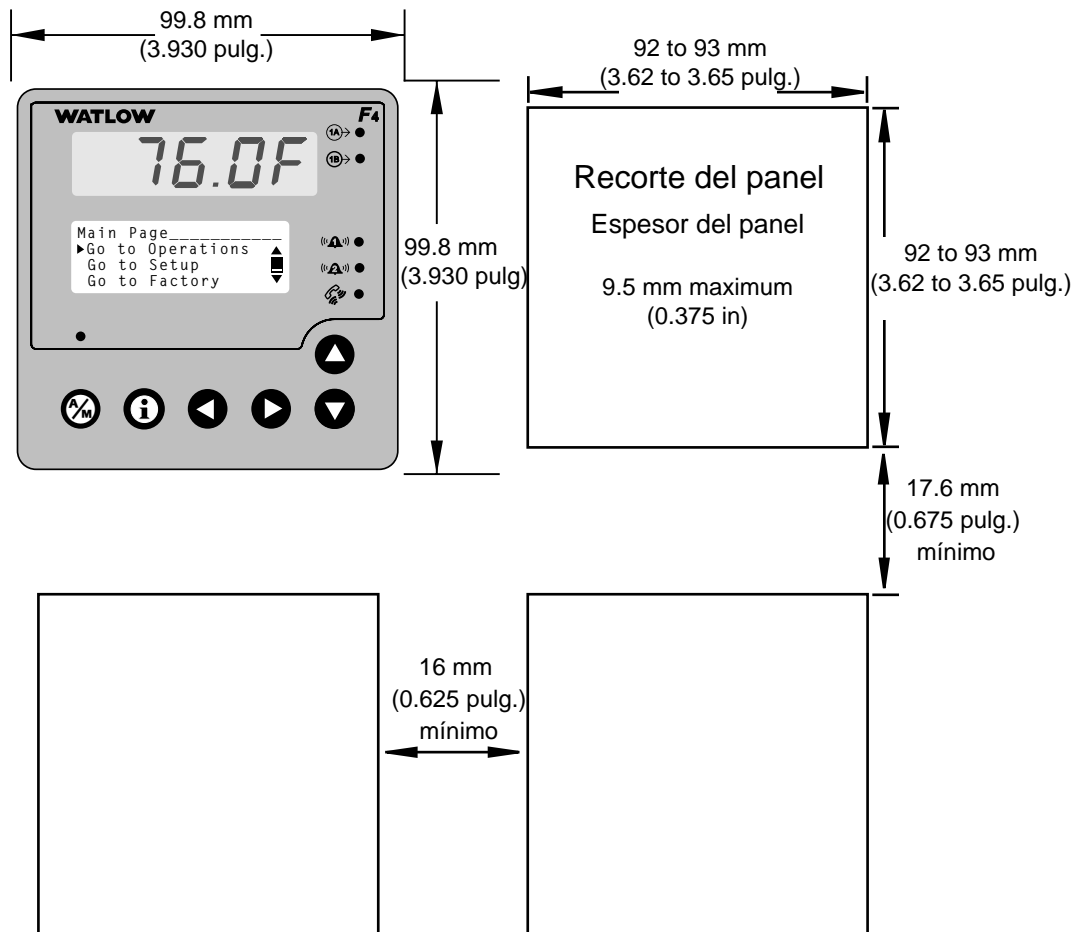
Dimensiones de cortes múltiples del panel.
